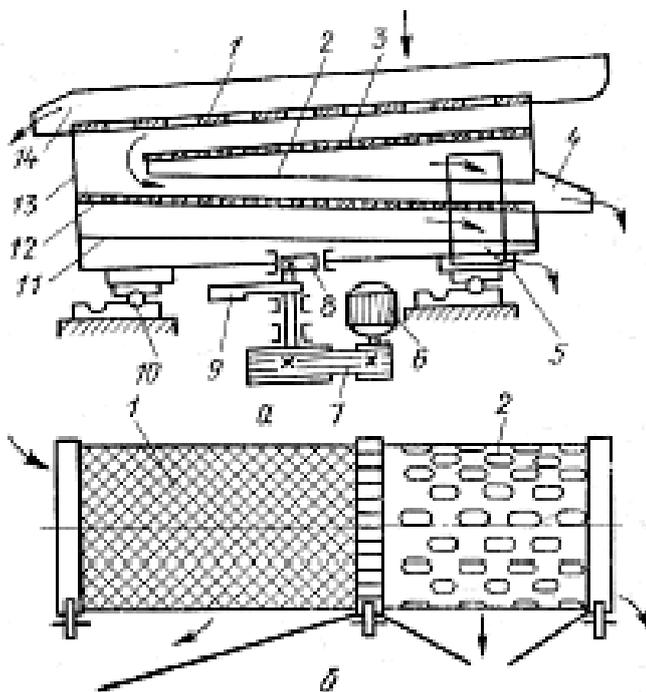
Установки для сортировки щепы: а- плоская; 1, 3, 12-сита; 4, 5, 14-лотки; 2, 11-поддоны; 6- электродвигатель; 7-ременная передача; 8-эксцентрик; 9-противовес; 10-шаровые опоры; 13-короб; б- барабанная
